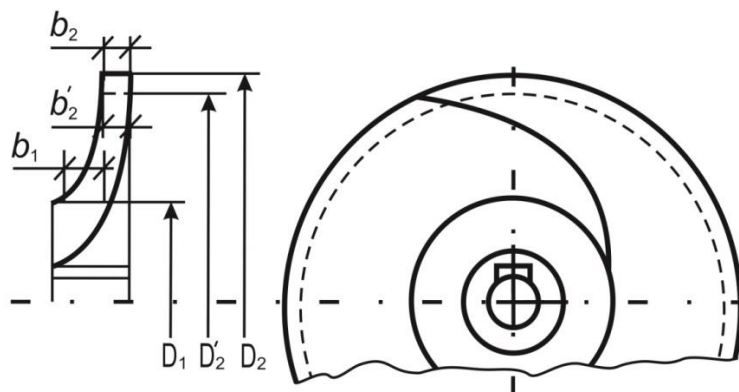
Обрезка рабочего колеса центробежного насоса [10]
